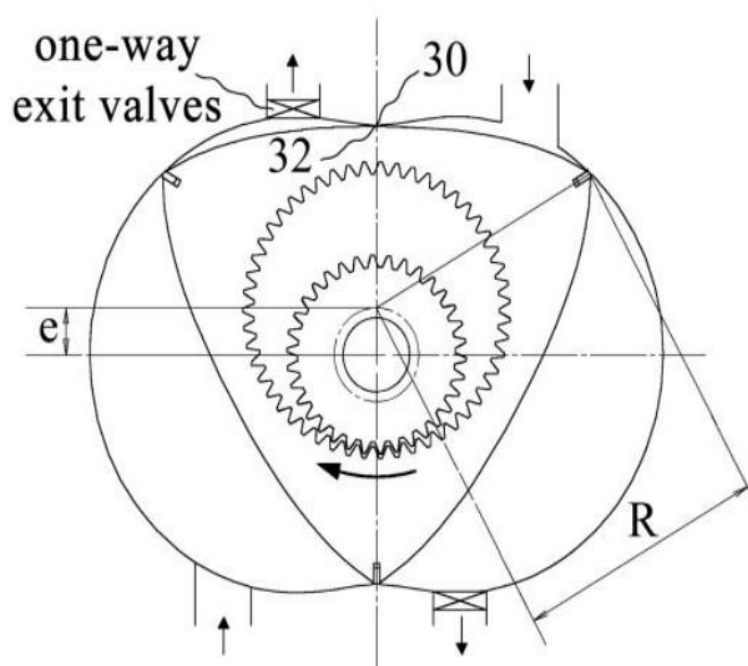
Вид в поперечном разрезе машины с ротором в положении ВМТ двигателя (верхняя мертвая точка).
